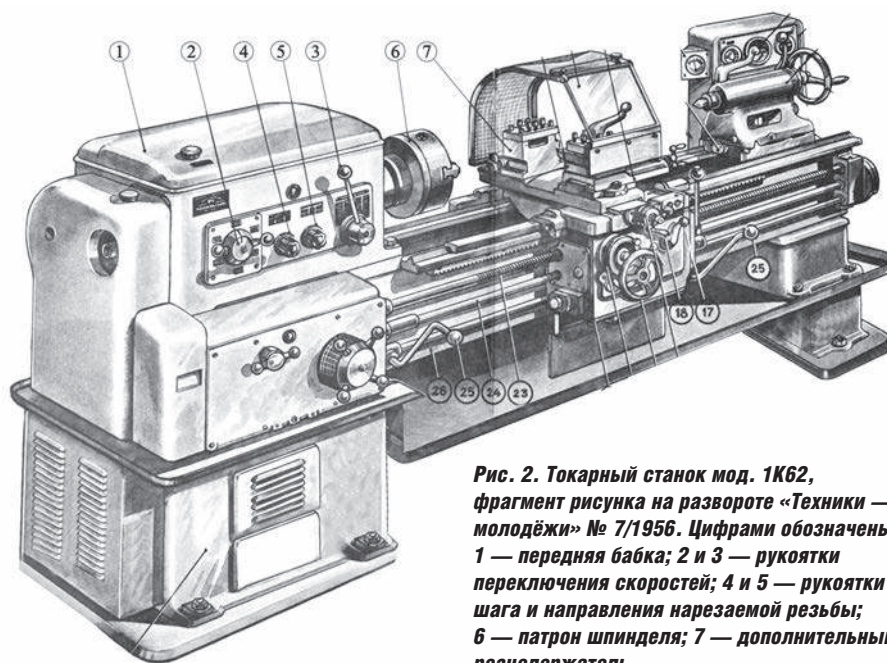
Токарный станок мод. 1К62, фрагмент рисунка на развороте «Техники — молодёжи» № 7/1956. Цифрами обозначены: 1 — передняя бабка; 2 и 3 — рукоятки переключения скоростей; 4 и 5 — рукоятки шага и направления нарезаемой резьбы; 6 — патрон шпинделя; 7 — дополнительный резцедержатель
